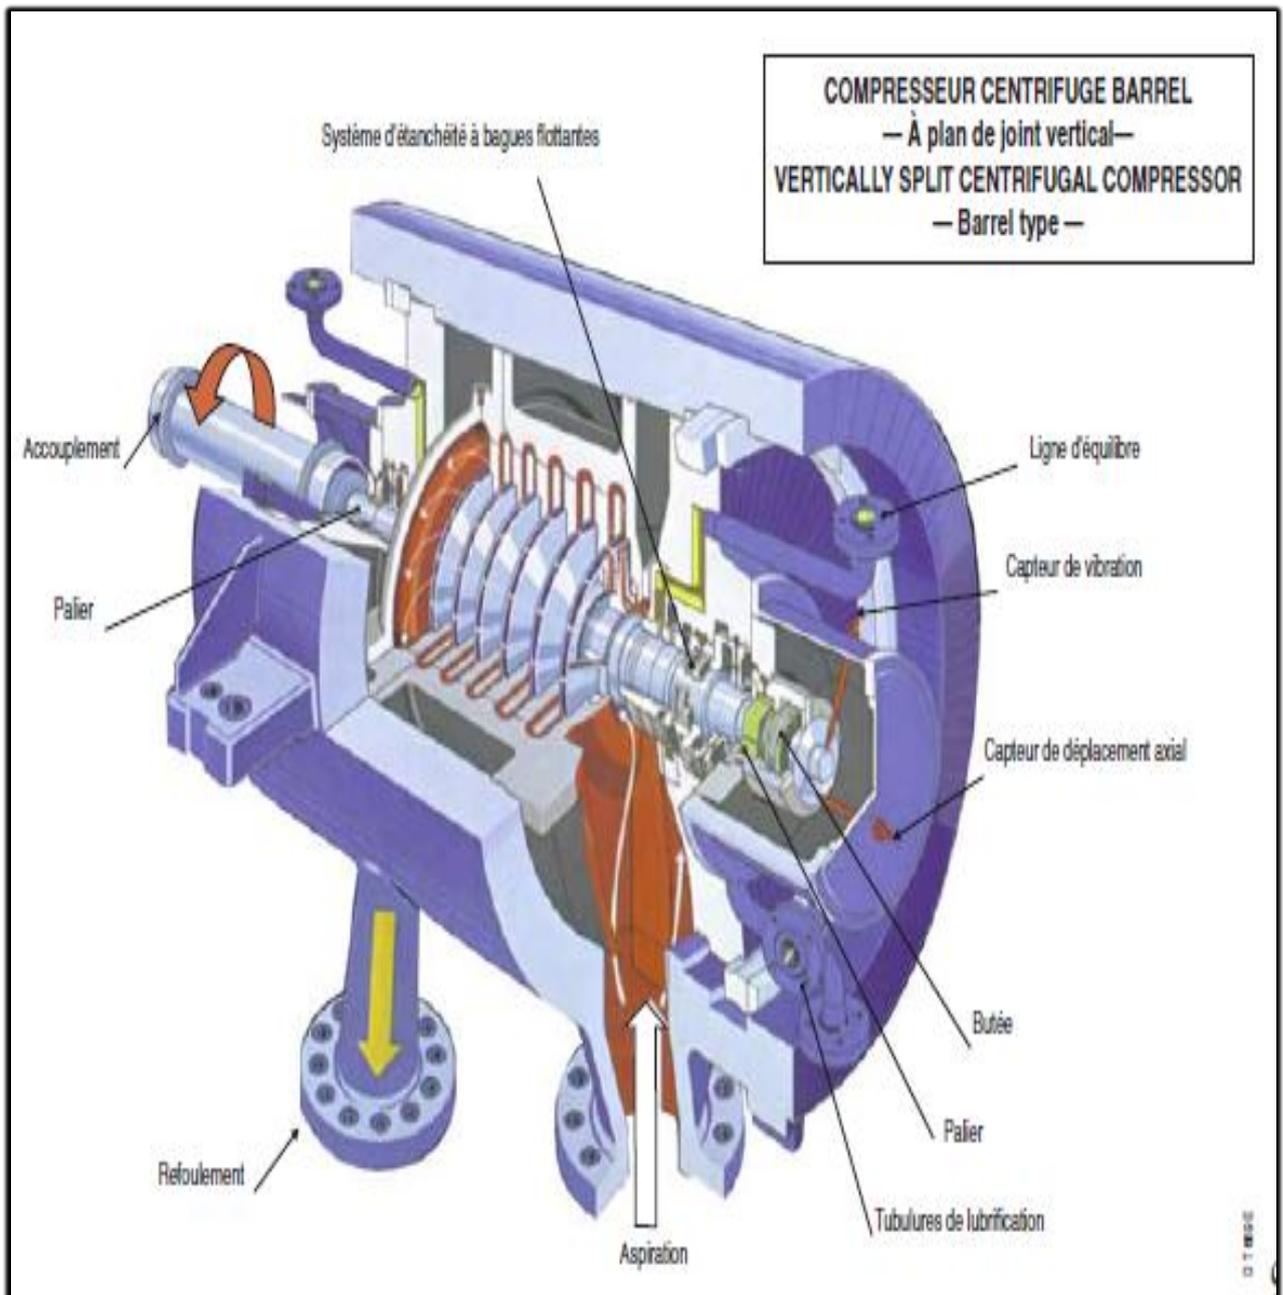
Compresseur centrifuge avec enveloppe à plan de joint vertical
